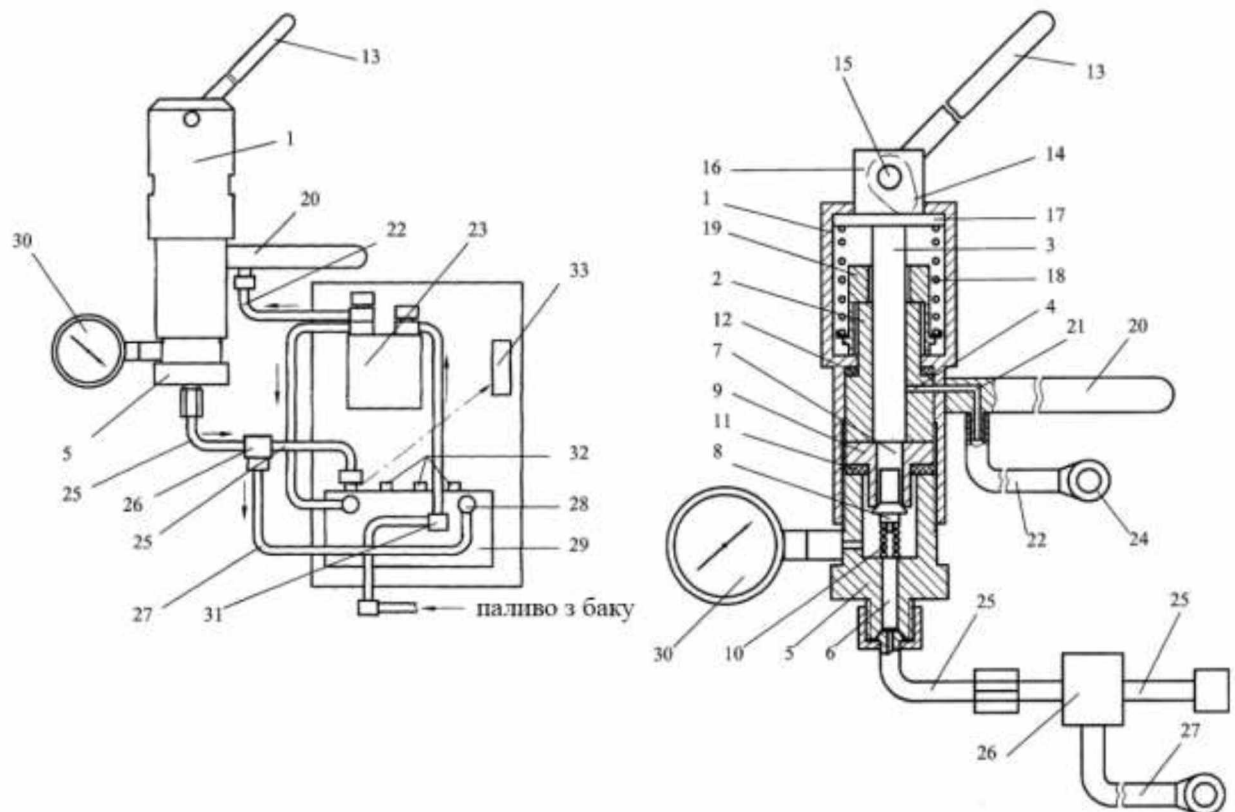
Пристрій для діагностування прецизійних пар паливного насоса і форсунок дизеля [17]: 1 – плунжерний насос; 2 – корпус-втулка; 3 –
